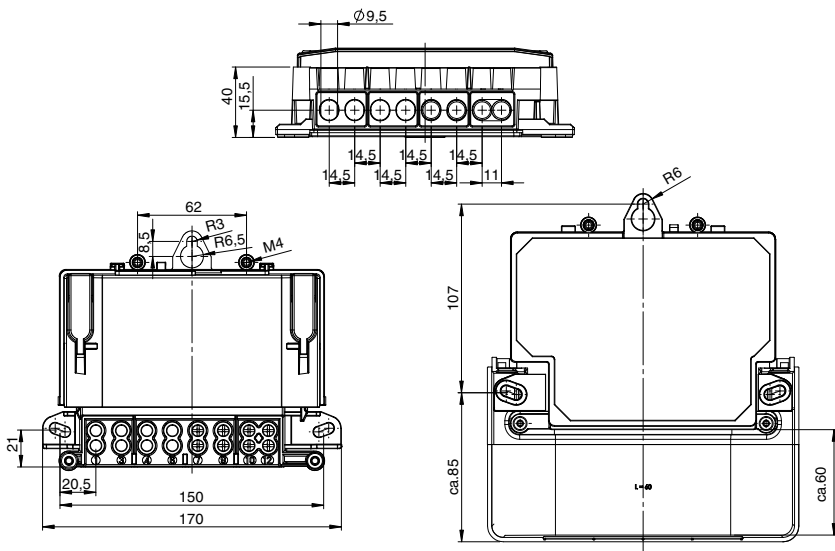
Maßblatt Q3D x2xxx, x3xxx (100- bzw. 60-Ampere-Ausführung mit Klemmendurchmesser 9,5 mm)
